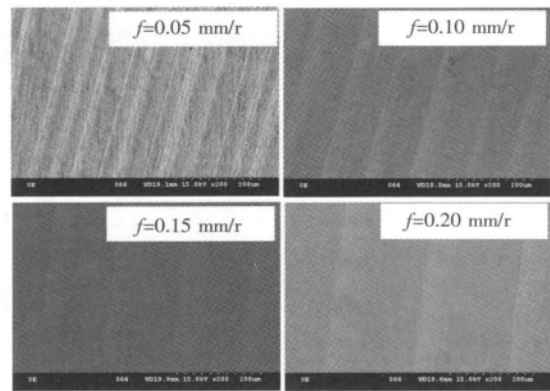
淬硬轴承钢 GCr15 精密切削加工表面形貌
